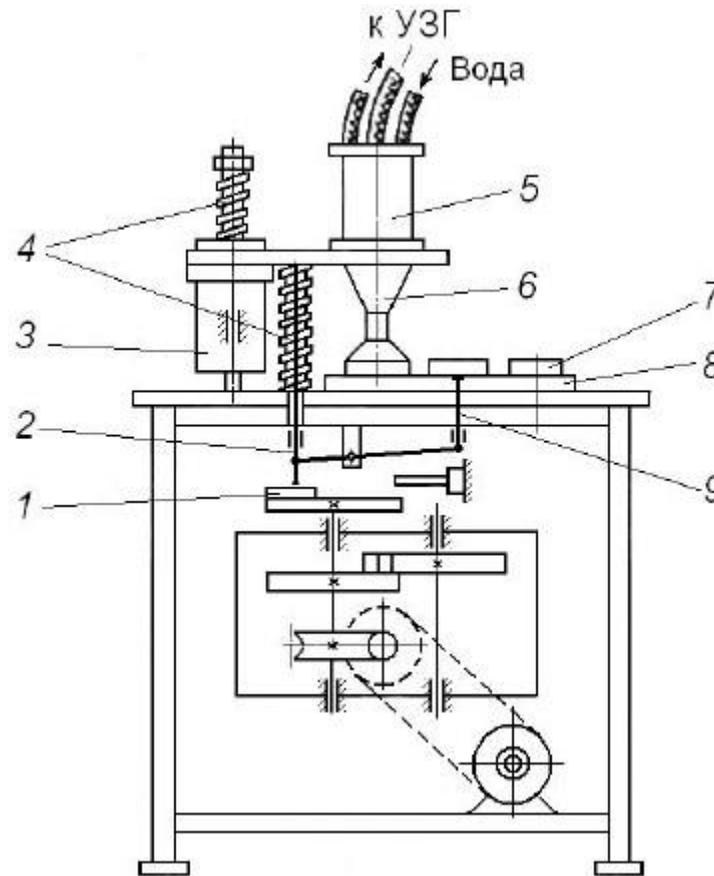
Устройство сварочной машины типа УПК.-15М1: 1 – выступ кулачка; 2, 9 – толкатели; 3 – кронштейн; 4 – пружины; 5 – сварочный узел (акустическая система); 6 – волновод-инструмент; 7 – опорный стакан; 8 – поворотный стол
